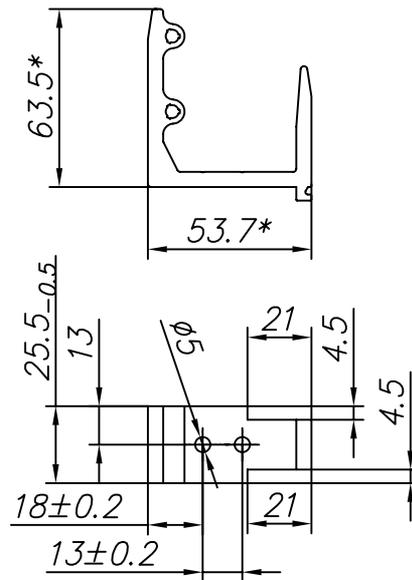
Изготовление соединителя FLGU.400.0913
